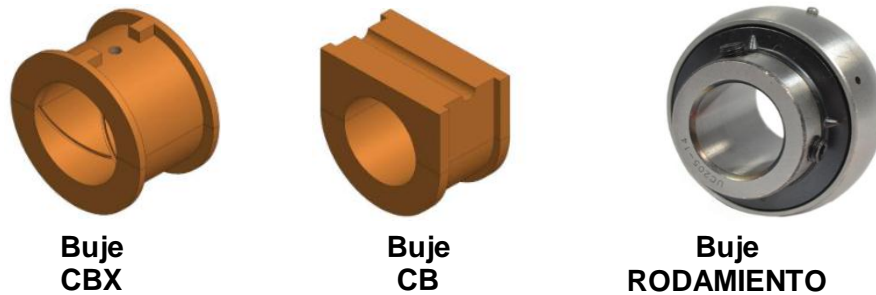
Tipos de Bujes – manual conveyor (engineering & manufacturing)
